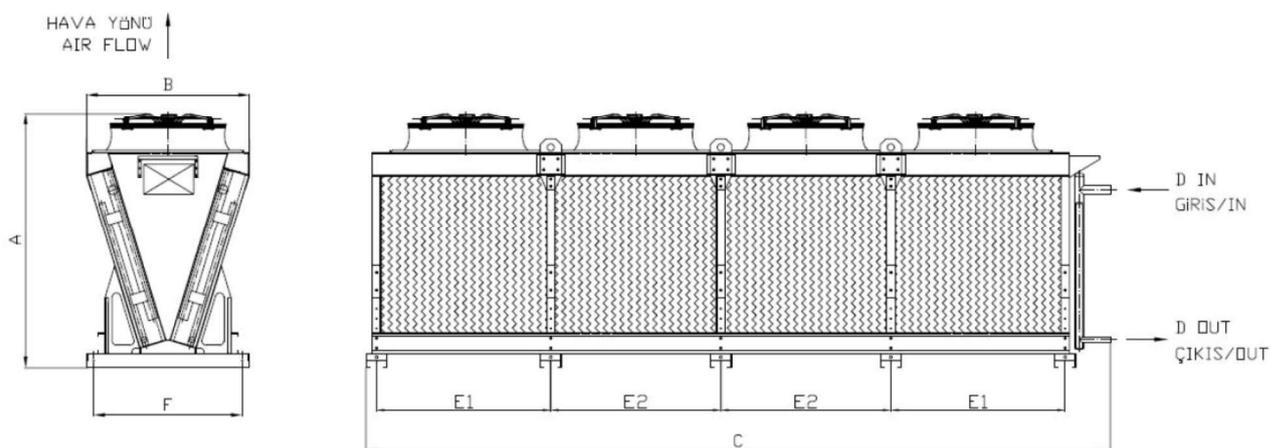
Габаритные размеры конденсатора КС-t-491FB1-B06 C2
